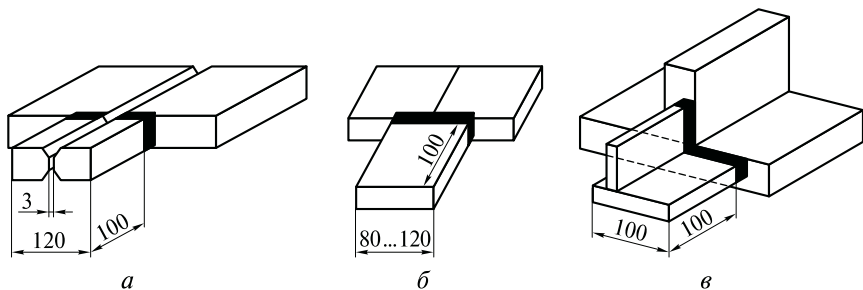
Входные и выходные планки для сварных швов:
